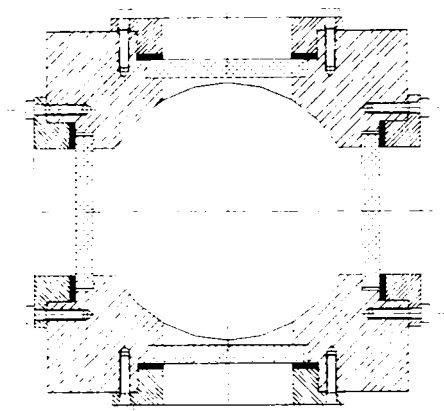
Secțiune transversală prin celula de testare 2
